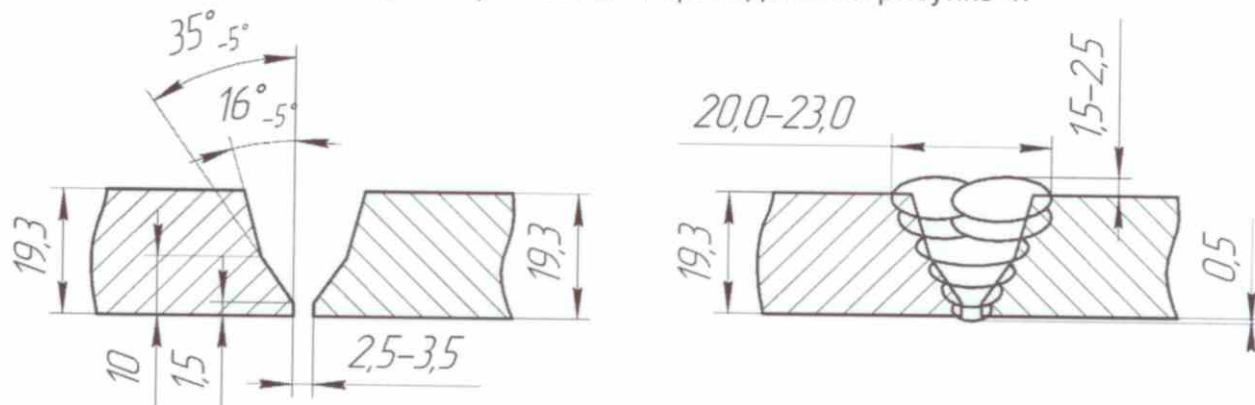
Геометрические параметры сборки и сварного шва
